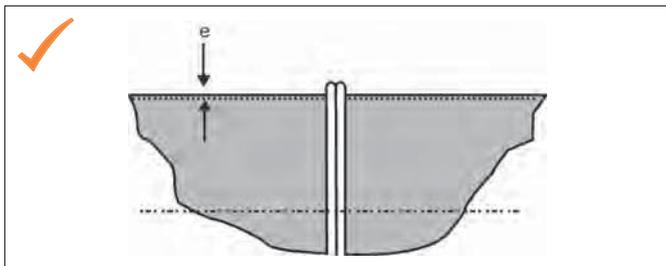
Schweißnaht mit gleichmäßige Wulstausbildung (OK)
